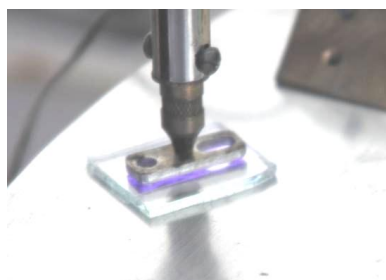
Подготовка образца при помощи анодной сварки
